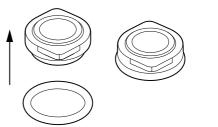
Montaje de la junta tórica en la parte fija del cierre
